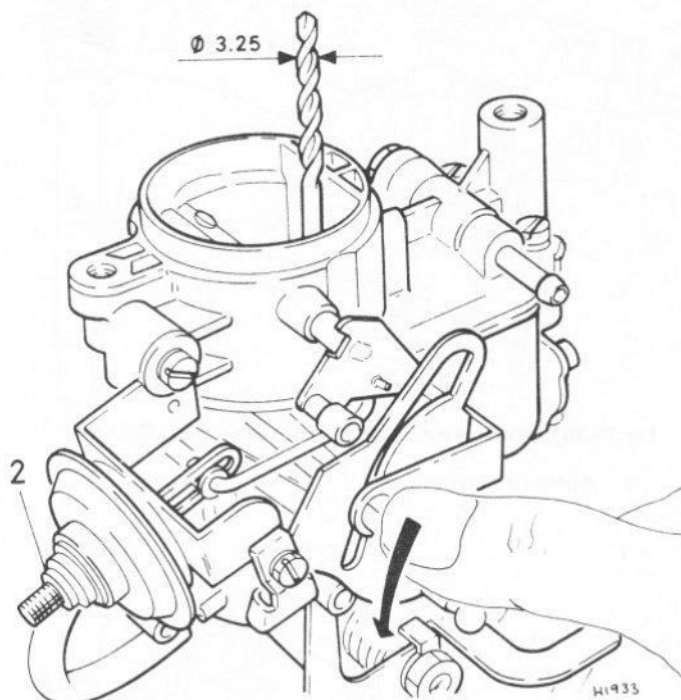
Régler l'ouverture de starter - carburateur Weber 35 IBSH (Sec 8)
